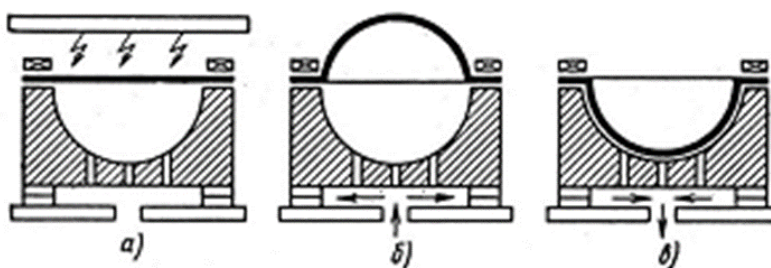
Схема негативного формування із попередньою пневматичною витяжкою
